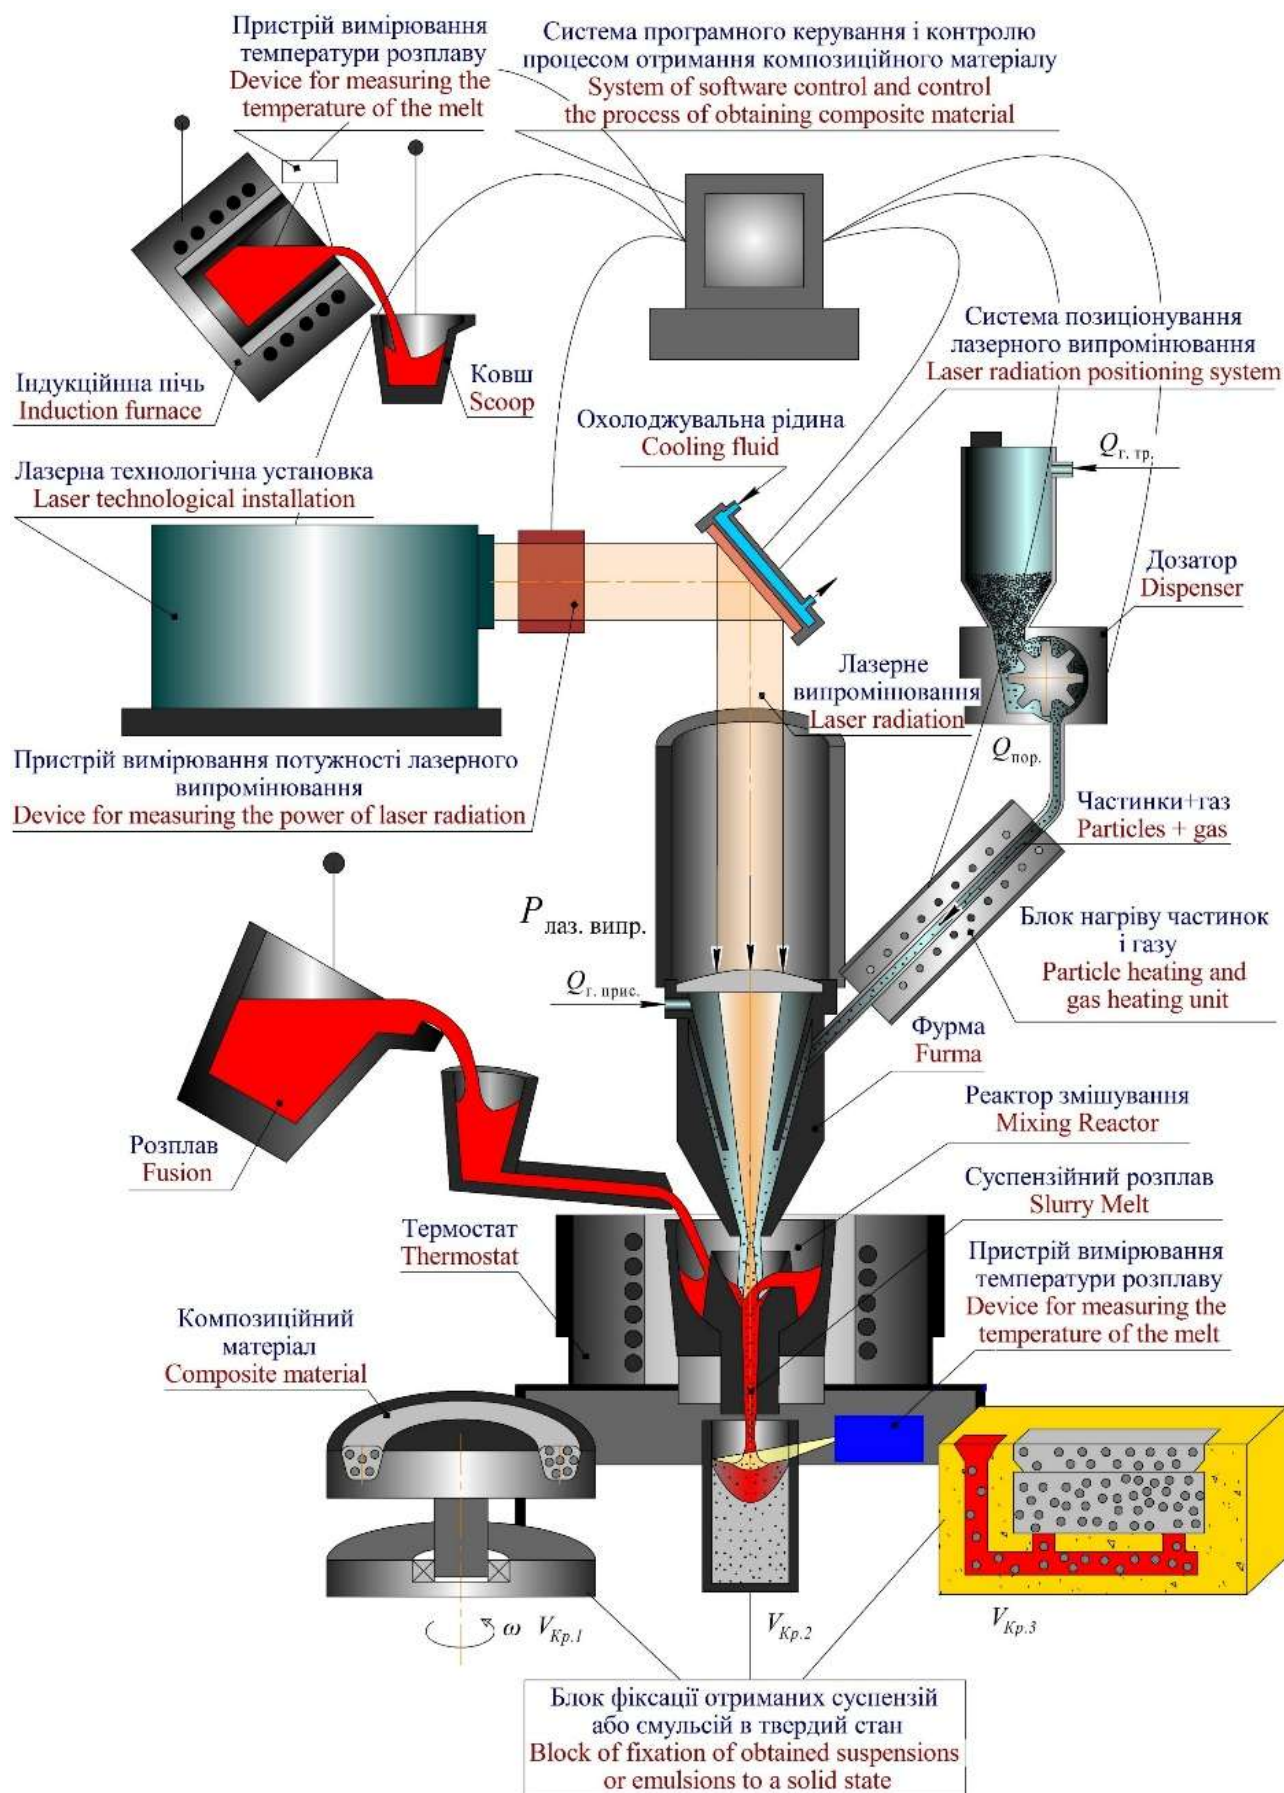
Схема установки гібридного лазерно-ливарного методу для отримання композиційного та пористого матеріалу
